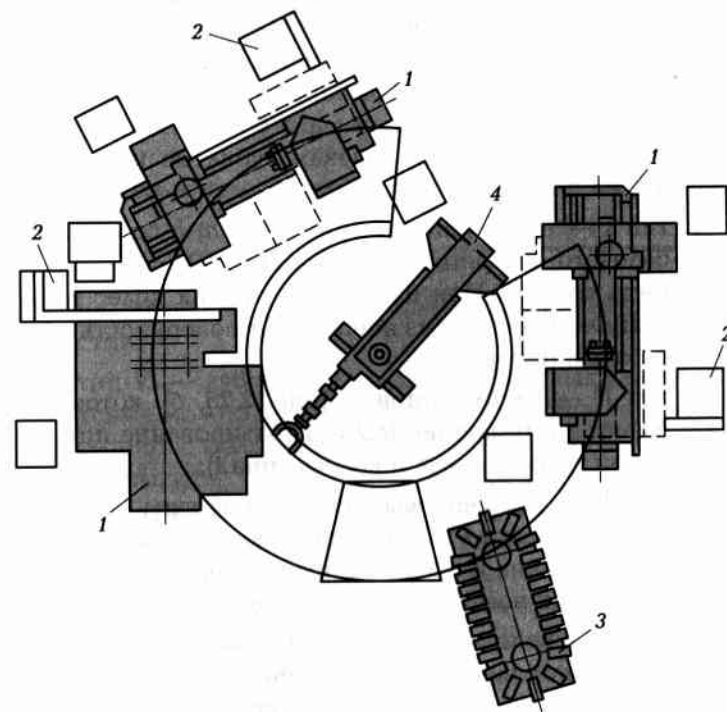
Многостаночный роботизированный технологический комплекс
